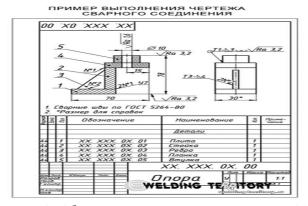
Обозначение сварного соединения по ГОСТ
